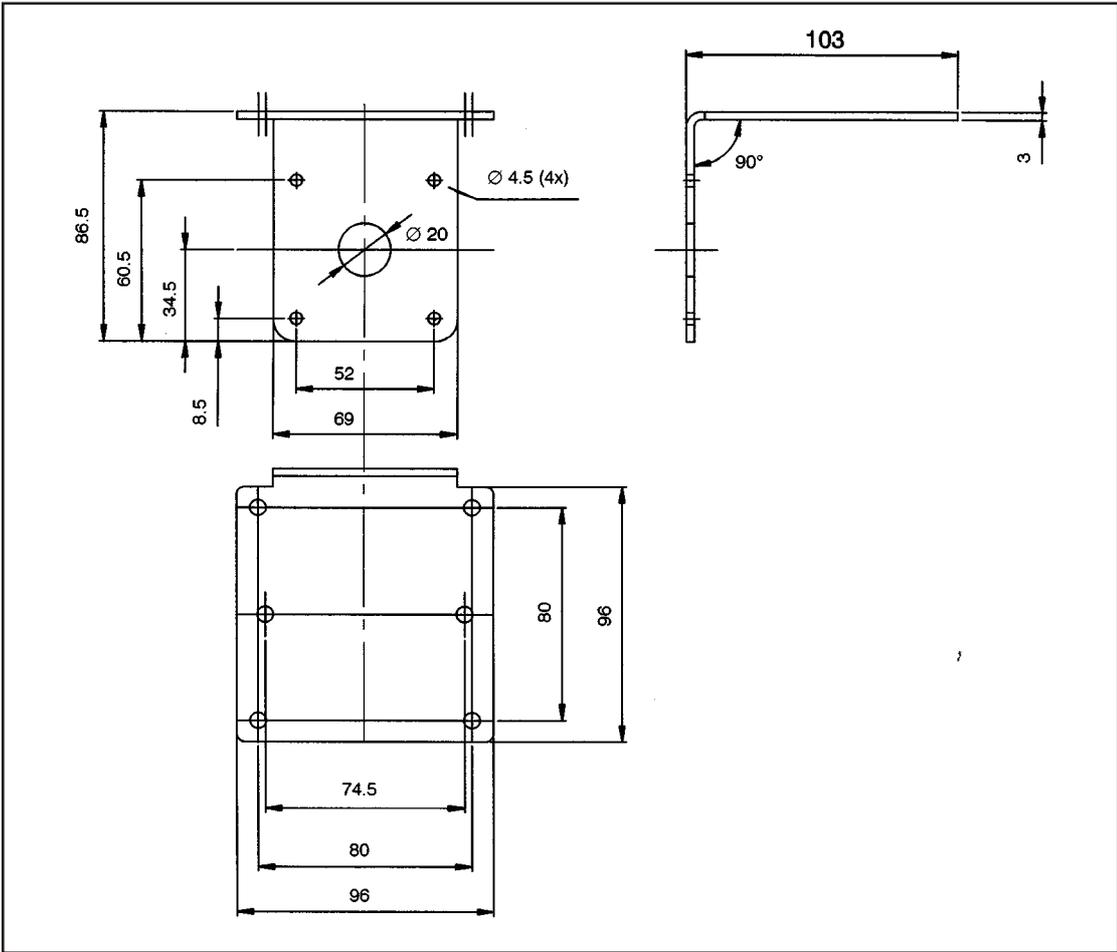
Dimensions de la plaque de montage du A4021A pour les Séries VQ400 et VE5000 (en millimètres).
